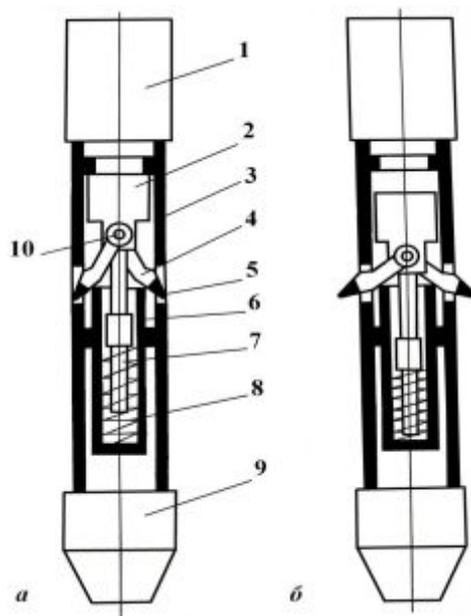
Схема разработанного фрезерного инструмента в транспортном (а) и рабочем (б) положениях: 1, 9 – центраторы, 2 – поршень, 3 – корпус, 4 – лопасть, 5 – твердосплавная пластина, 6 – внутренняя труба, 7 – толкатель, 8 – пружина, 10 – ось
